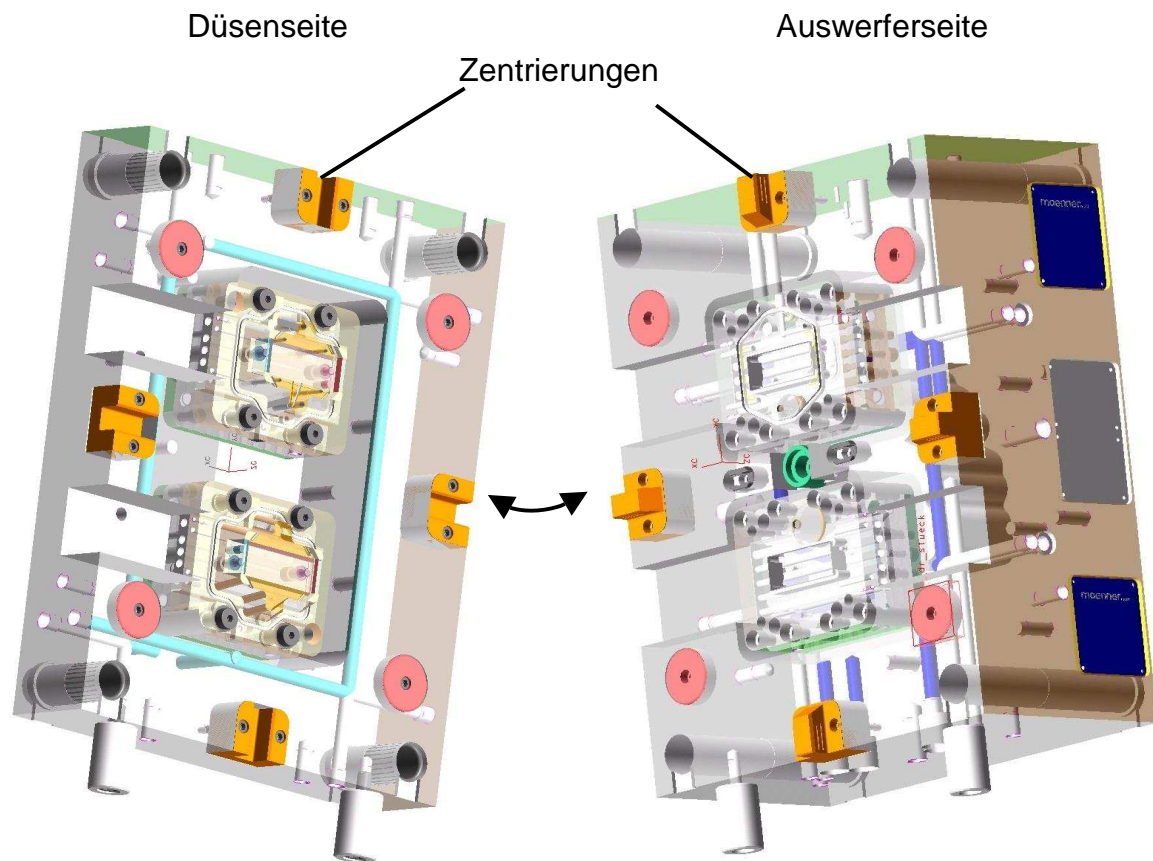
3D-Konstruktionszeichnung des Indexplatten-Werkzeuges
